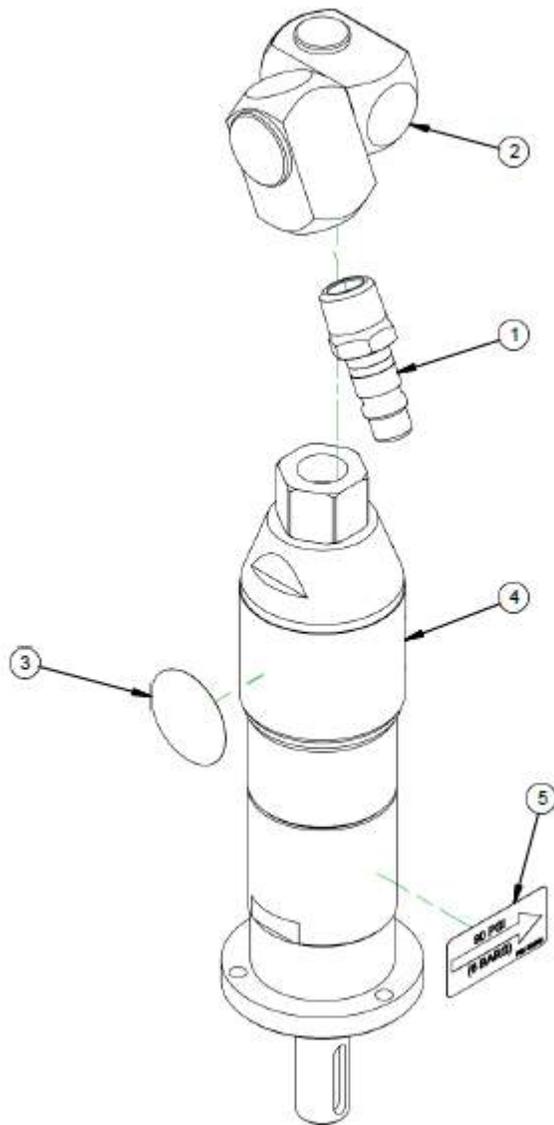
ENSEMBLE DE CONDITIONNEMENT PNEUMATIQUE (PCU) (RÉF. 78264)
